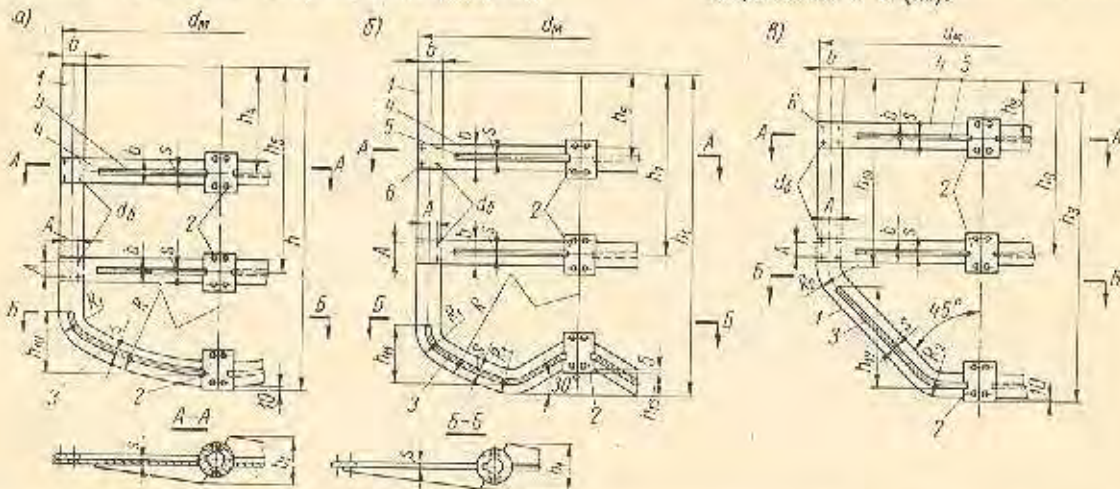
Конструкции стальных сварных рамных перемешивающих устройств (тип 6) по МН 5674—66: а — шифр 41; б — шифр 42; г — шифр 43.
